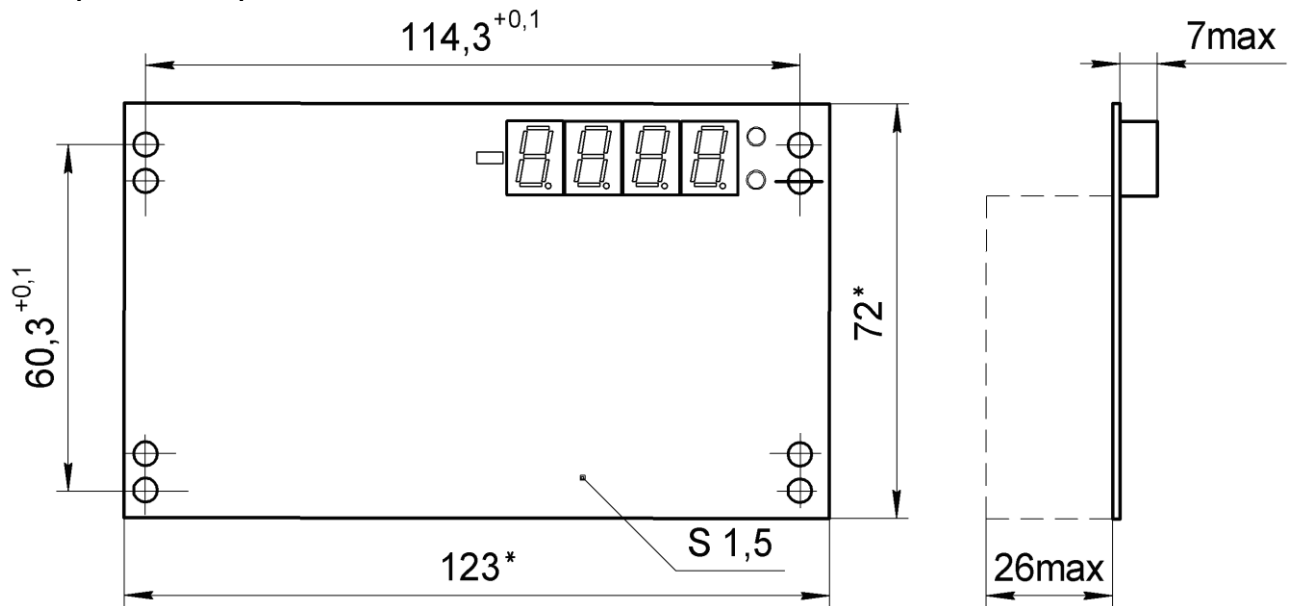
Габаритные размеры ИТМ-1-10
